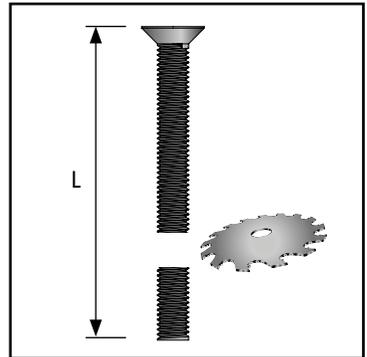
, lange M8-Schraube in der Länge ggf. anpassen
